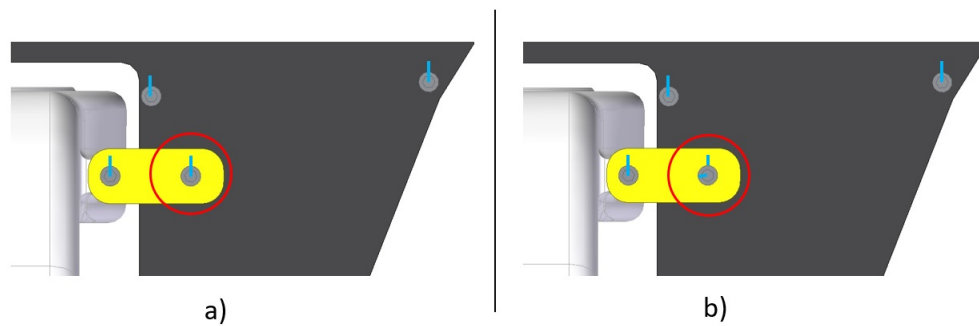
Ensamble tornillo con superficie de contacto a) Alineado b) Desalineado
